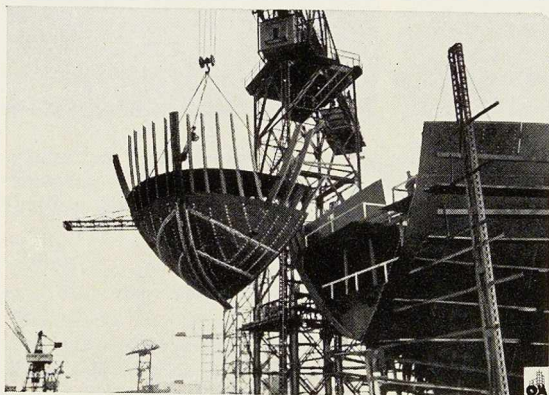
Élément de poupe préfabriqué et soudé amené sur la coulisse de montage.
